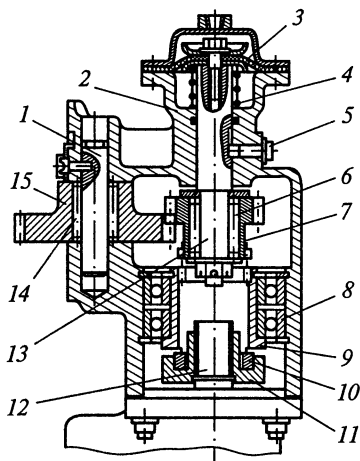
Коробка отбора мощности самосвалов КамАЗ: 1, 13 — оси; 2 — картер; 3 — диафрагма; 4 — пружина; 5 — винт; 6, 8, 14 — подшипники; 7, 15 — шестерни; 9 — полумуфта; 10 — призма; 11 — муфта; 12 — вал
